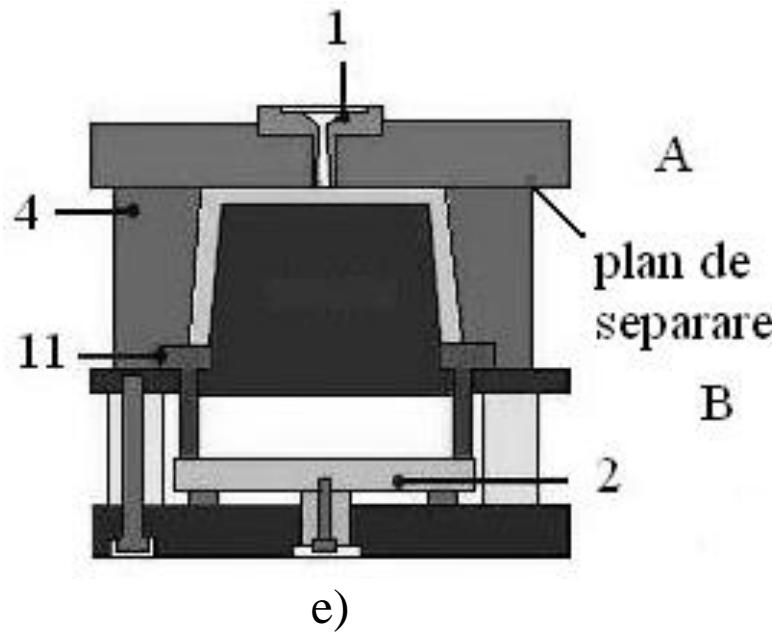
Exemple de forme de injecție: A – partea fixă a formei, B – partea mobilă
